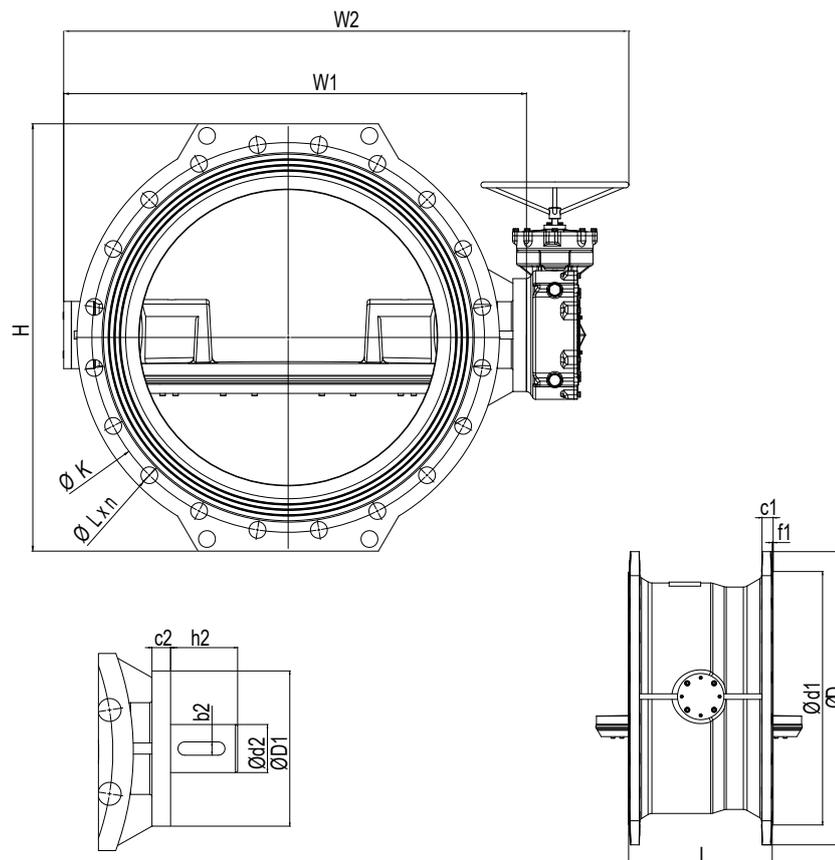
Disegno di sezione PN 16 DN 900 - 1800
